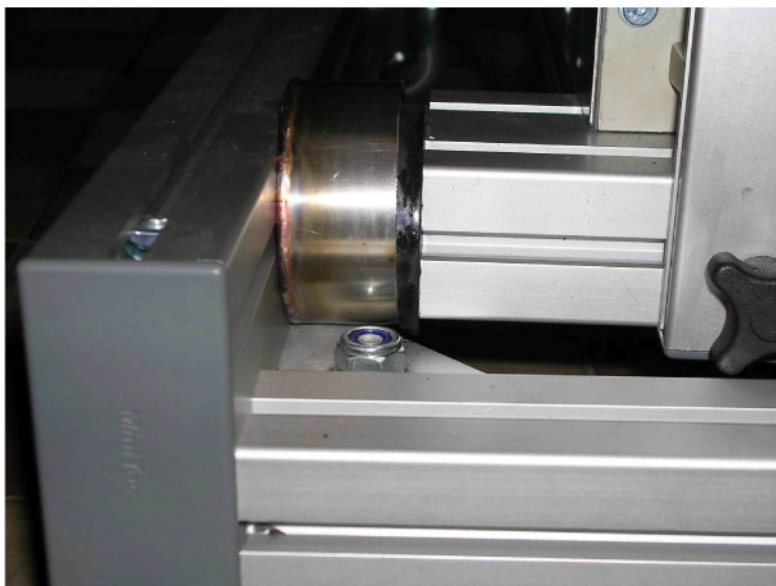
Smontovaná konstrukce – pohled ze zadu
